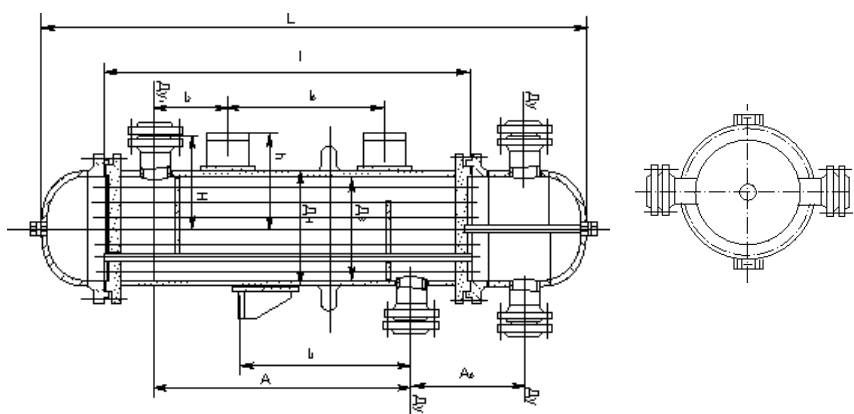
Аппараты кожухотрубчатые с неподвижными трубными решетками многоходовые
